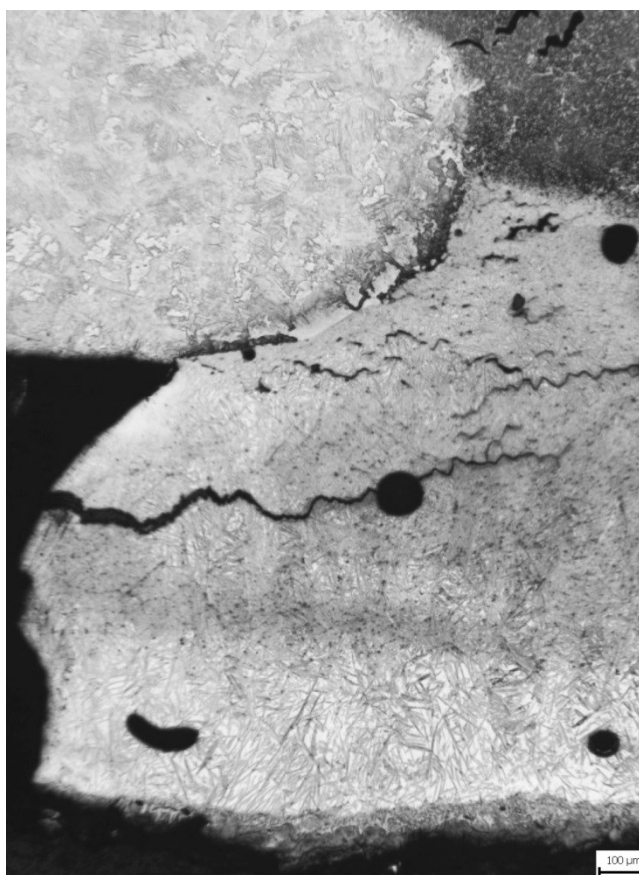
Detail oblasti přetečení svarového kovu vzorku 2A
